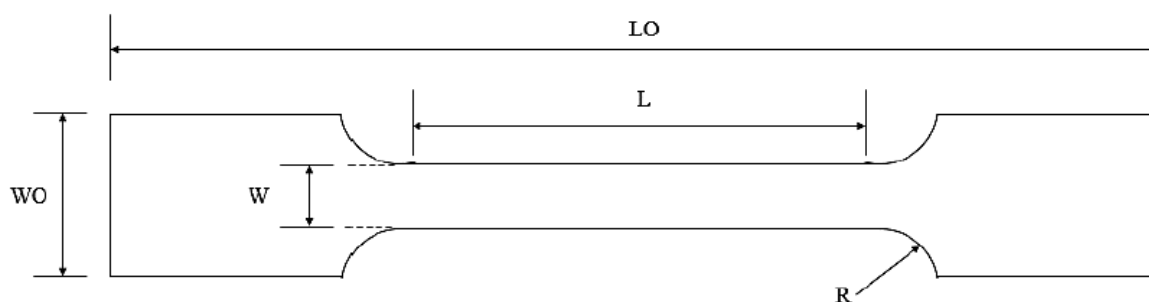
Схематичне креслення зразка для розтягу з розмірними орієнтирами для стандарту ASTM D638
